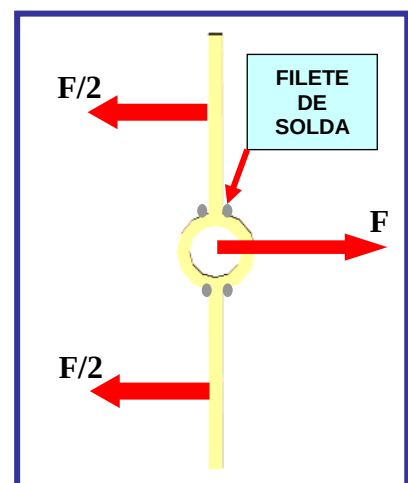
Esforços sobre os filetes de solda do eixo do carro guia.
